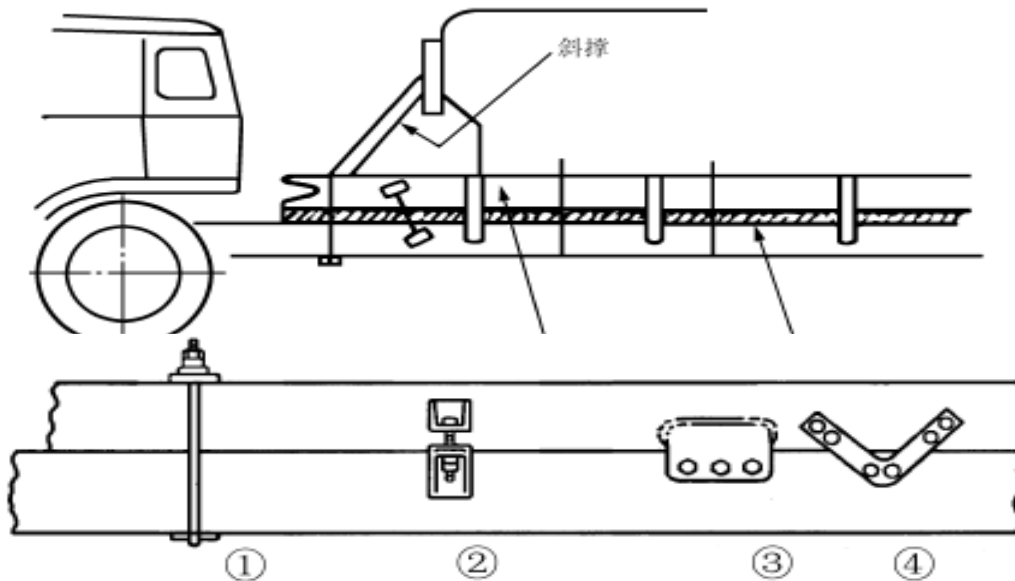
Disposición de las vigas longitudinales del bastidor auxiliar
